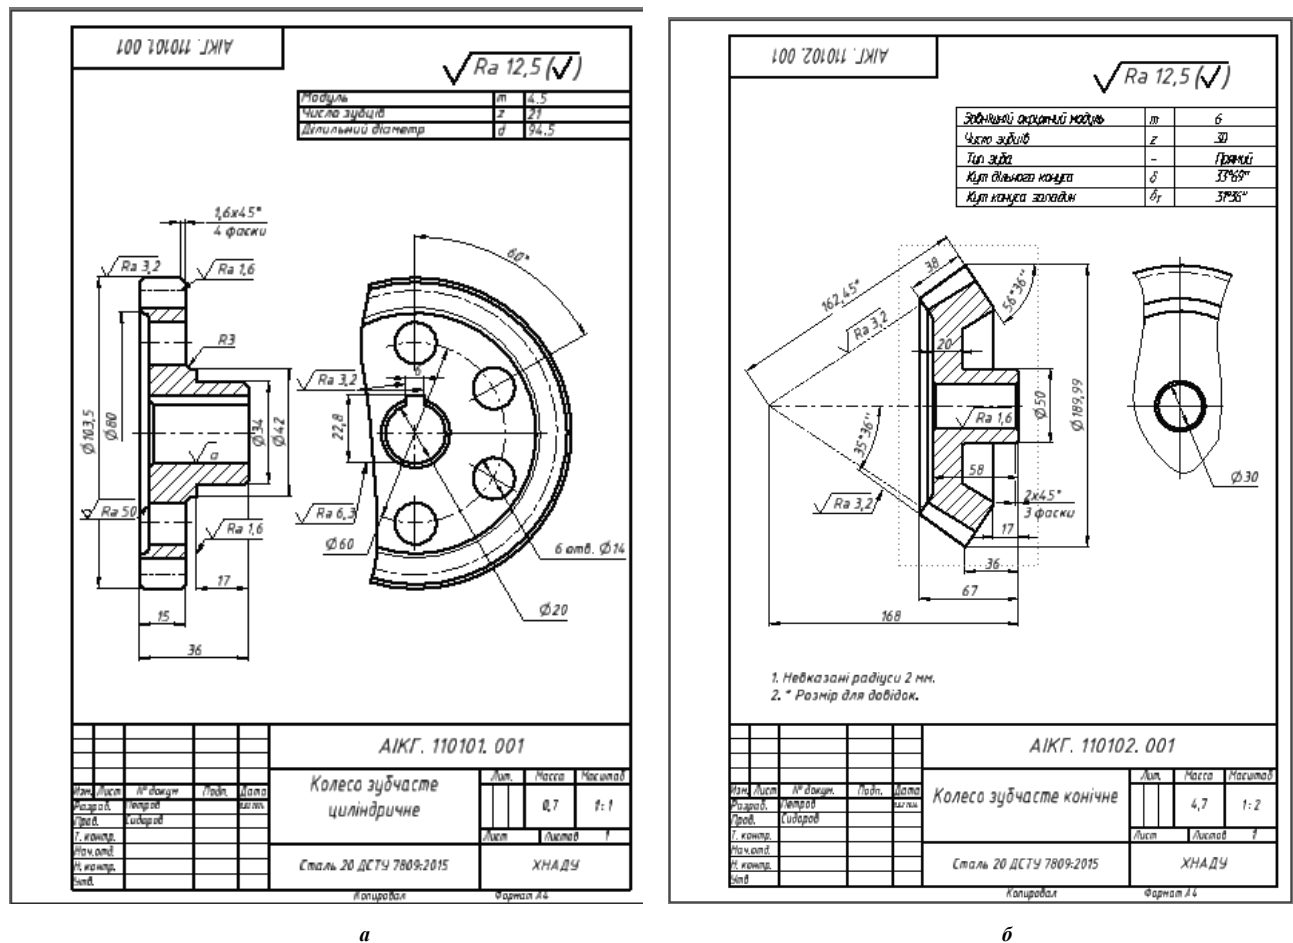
Кресленик циліндричного та конічного зубчастого колеса
